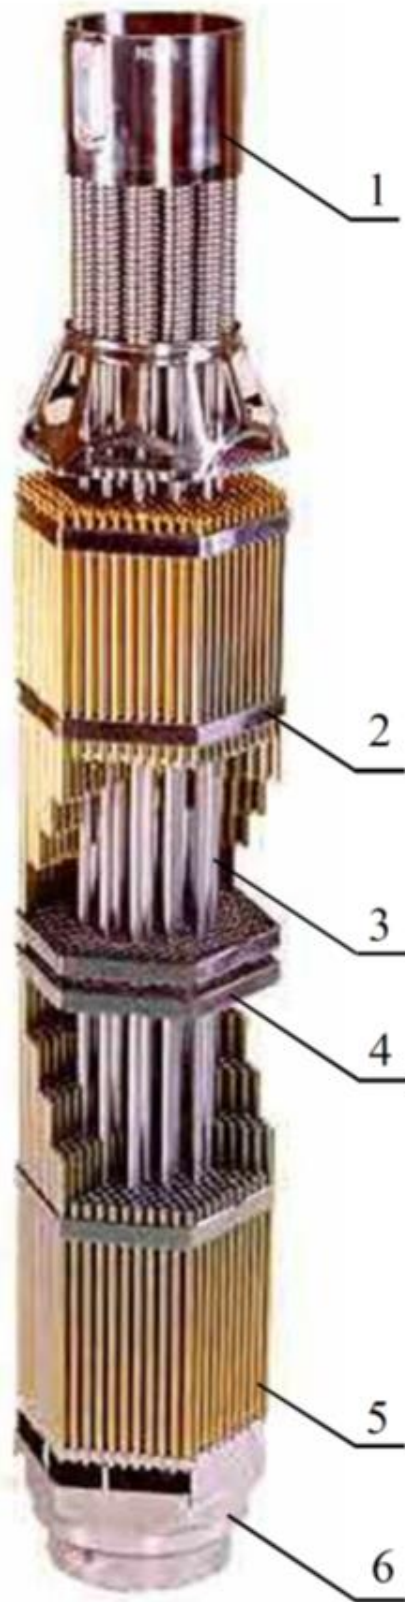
Конструкція паливної касети реактора ВВЕР-1000:
